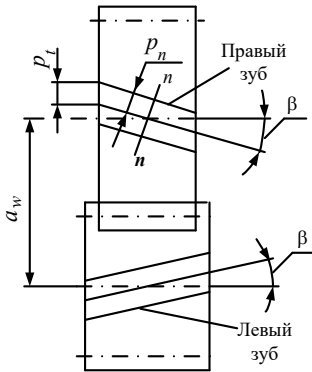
Схема косозубой цилиндрической передачи:
